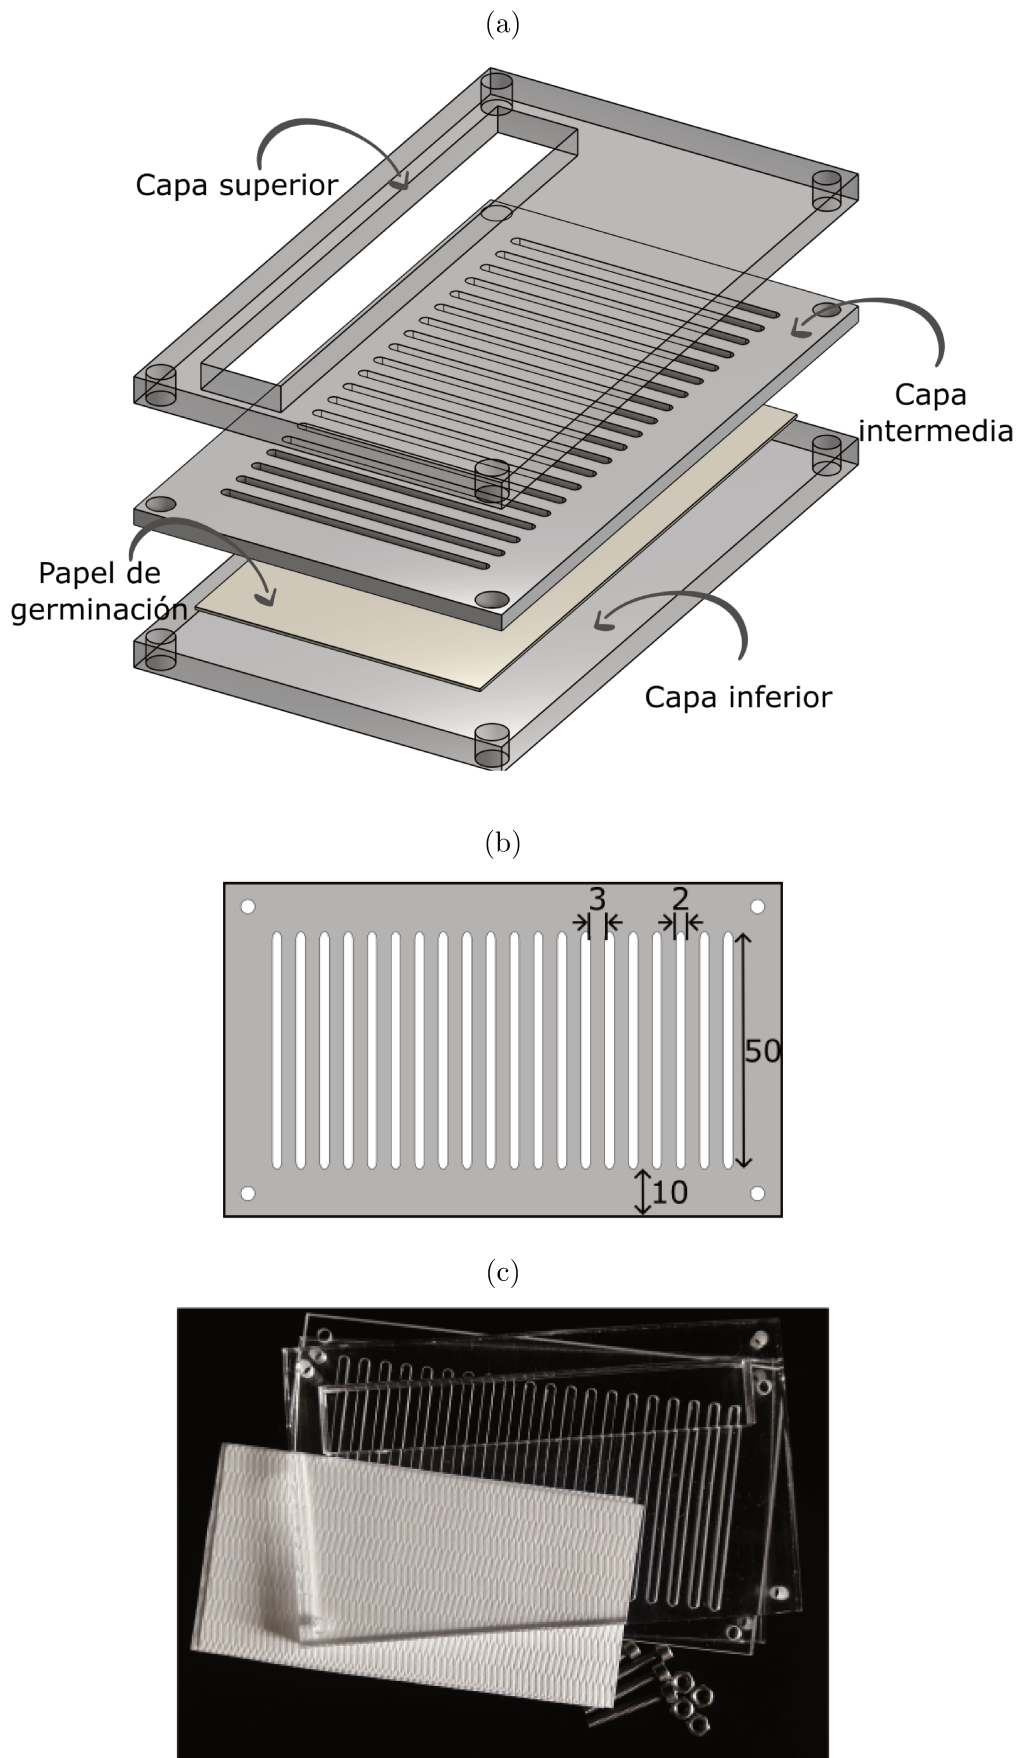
Prototipo 1. (a) Vista expandida del sistema multicapa. (b) Detalles de la capa intermedia con las 20 ranuras, las dimensiones están en mm. (c) Imagen de los componentes del dispositivo sin ensamblar.
